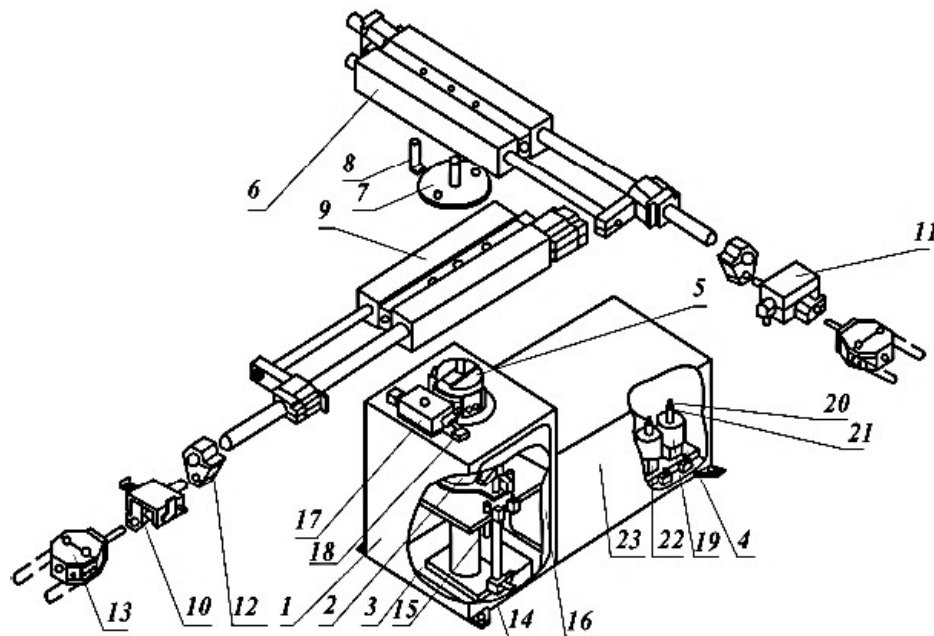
Схема розташування основних вузлів та елементів пневматичного промислового маніпулятора МП - 9С 1 – корпус маніпулятора; 2 – механізм підйому; 3 – механізм повороту; 4 – розподільна плита; 5 – муфта зубчаста; 6,9 - модуль поступальний (рука); 7 – фланець кріплення рук; 8 – колонка фіксації рук щодо фланця; 10 - модуль поступальний рух схоплювача; 11 - модуль повороту (ротації) схоплювача; 12 – кронштейн; 13 - схоплювач; 14 - упор; 15 – демпфер; 16 – кришка корпусу, 17 – амортизатор механізму повороту, 18 – контакт магнітокерований КЕМ; 19 – електромагнітний регулятор (дросель); 20 – голка; 21 - гайка фіксації голки; 22 -пневмодросель; 23 - корпус пристрою розподілу повітря.
